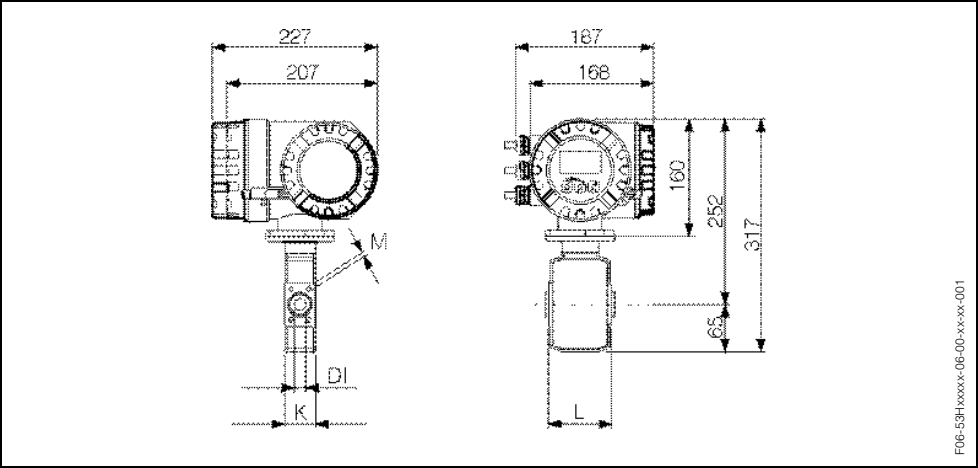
Dimensiones Promag H / DN 2...25 (versión compacta, cabezal de aluminio para montaje en campo)
